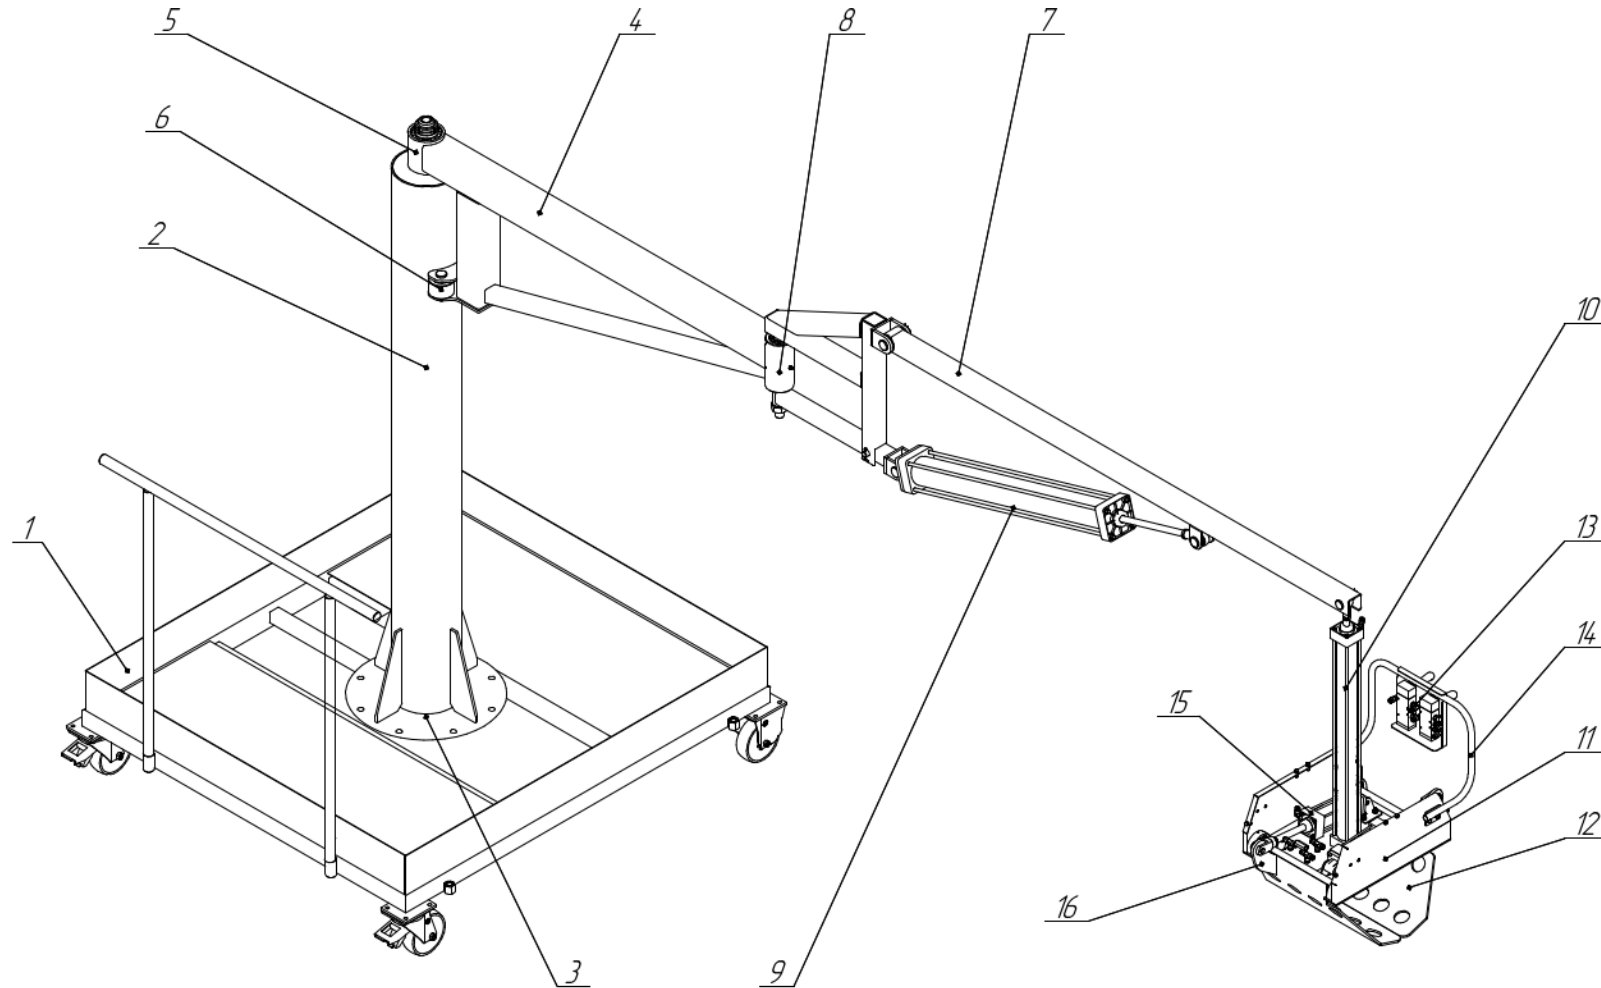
Рама с ручкой и колесами, 2 – колонна, 3 – соединительные фланцы, 4 - поворотная стрела, 5 - подшипниковый узел, 6 - блок опорных роликов, 7 - подъемно-поворотная консоль, 8 – подшипниковый узел подъемно-поворотной консоли, 9 – пневмоцилиндр подъема-опускание поворотной консоли ПЦ1 (см. рис.3), 10 - пневмоцилиндр подъема-опускание блока зажимов ПЦ2, (см. рис.3), 11 – блок зажимов с пневмоцилиндрами ПЦ3, 12 – затіскачі, 13 – блок управления пневмоцилиндрами, 14 - ручка управляющая, 15 – пневмоцилиндры ПЦ3 привода зажимов, 16 - система рычага поворота зажимов
